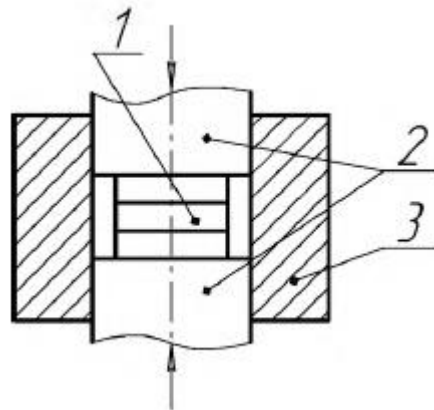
Переформування заготовок осаджуванням 1 - пакет заготовок; 2 - пуансон; 3 – матриця
